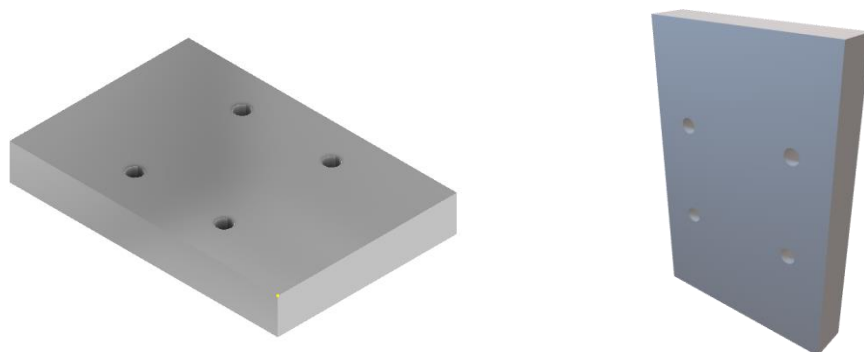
Τρισδιάστατη απεικόνιση αποστολής 14
